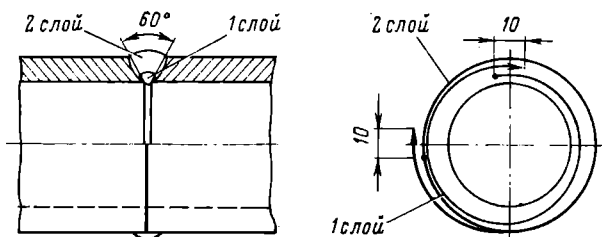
Схема стыкового сварного соединения экранной трубы диаметром 51×2,5 мм
